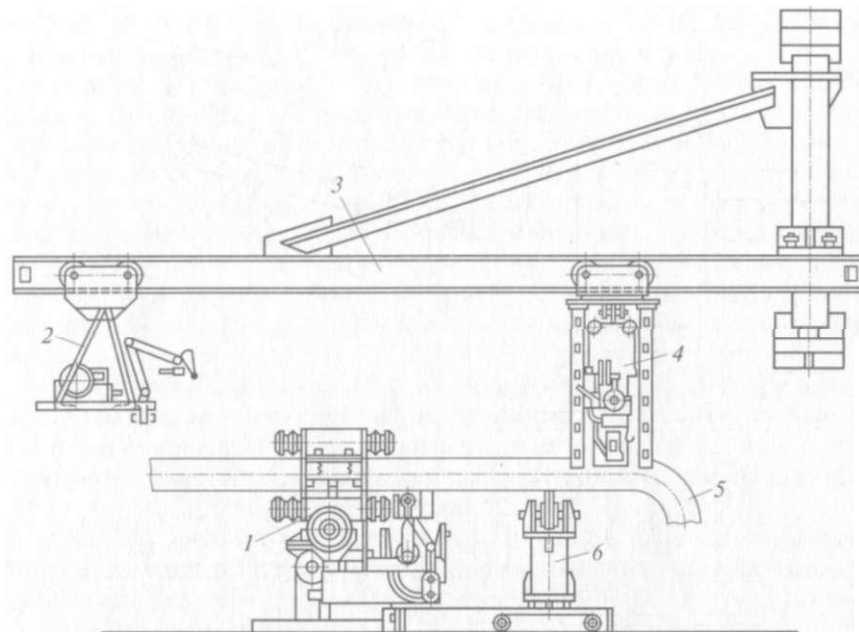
Пост для полуавтоматической сварки элементов с $D = 50 \dots 500$ мм:
